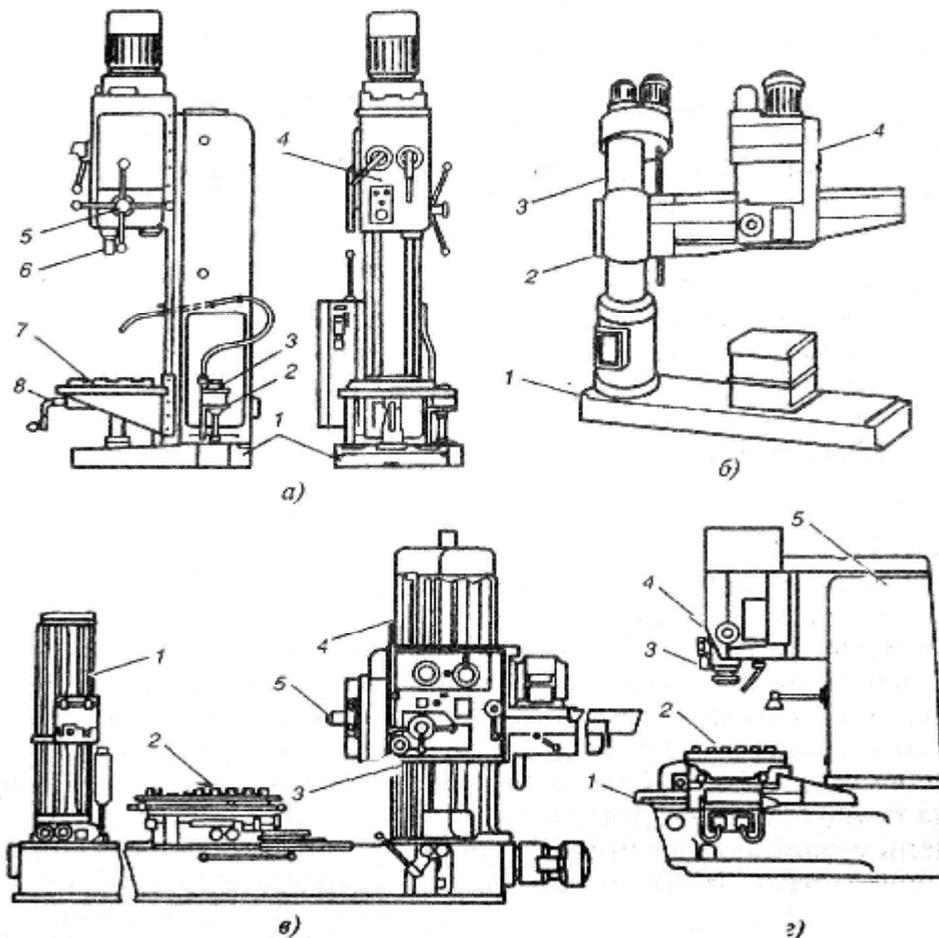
Станки сверлильно-расточной группы: *а* – вертикально-сверлильный (1 – станина; 2 – насос; 3 – фильтр; 4 – головка сверлильная; 5 – рукоятка; 6 – шпиндель; 7 – стол; 8 – привод подъема стола); *б* – радиально-сверлильный (1 – станина; 2 – траверса поворотная; 3 – колонна; 4 – головка сверлильная); *в* – горизонтально-расточной (2 – суппорт с поворотным столом; 3 – бабка шпиндельная; 4 – стойка; 5 – шпиндель расточной); *г* – координатно-расточной (1 – крестовый стол; 2 – стол; 3 – контрольное устройство; 4 – головка шпиндельная; 5 – станина)
